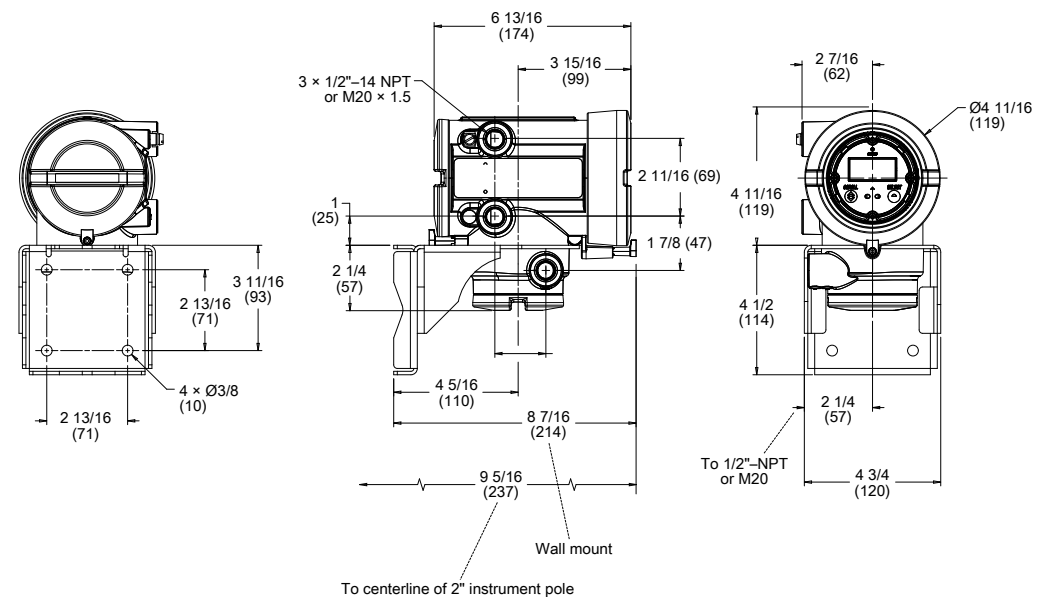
Dimensiones del transmisor de montaje remoto de 9 hilos (carcasa de aluminio recubierto)
